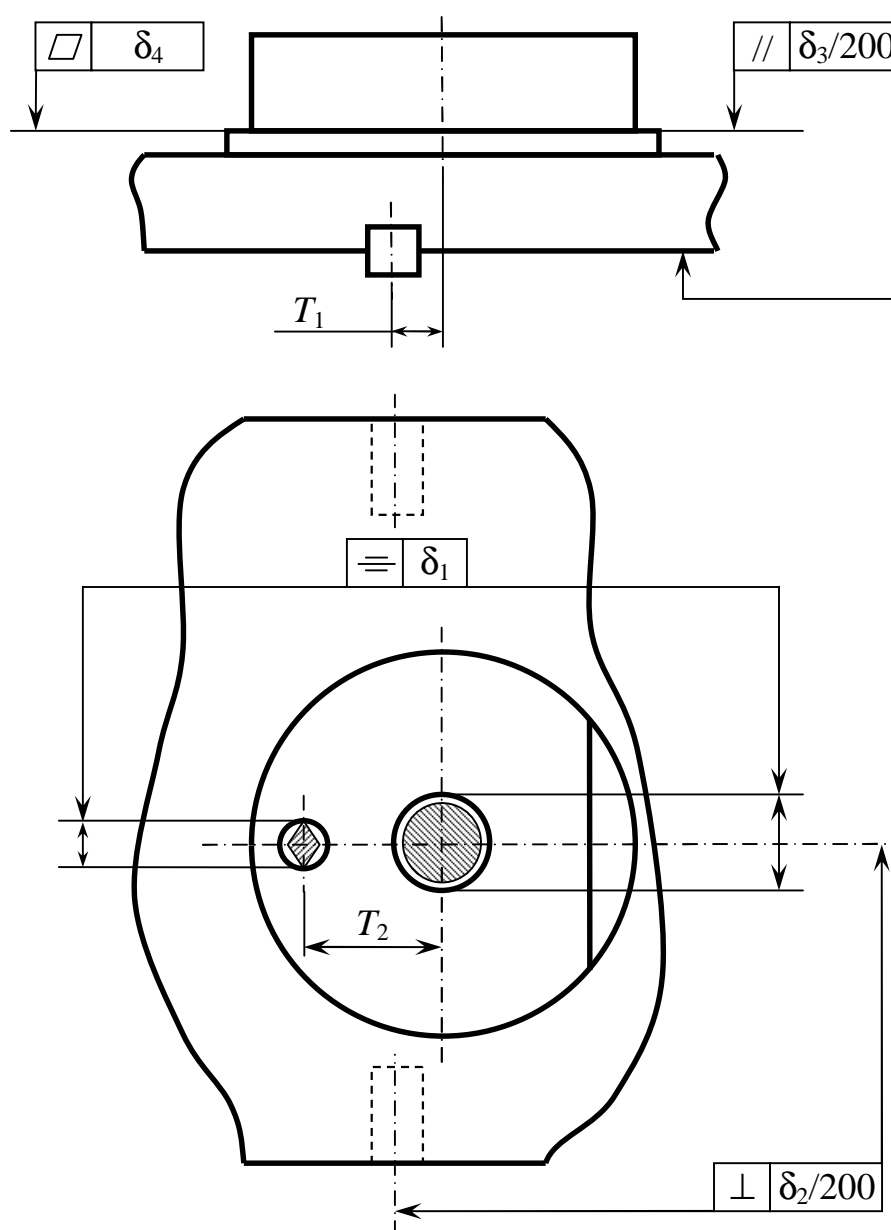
Допуски формы и расположения в конструкции приспособления
